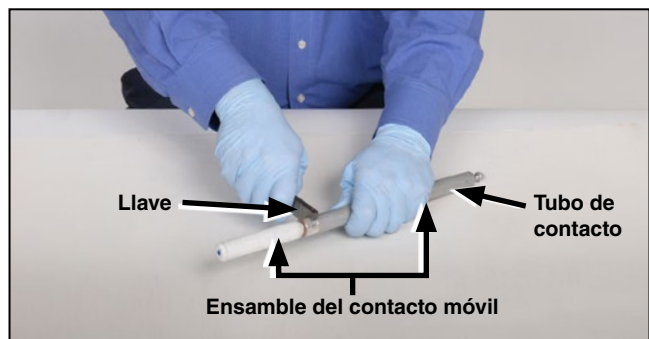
Desatornille el tubo de contacto del contacto móvil.
